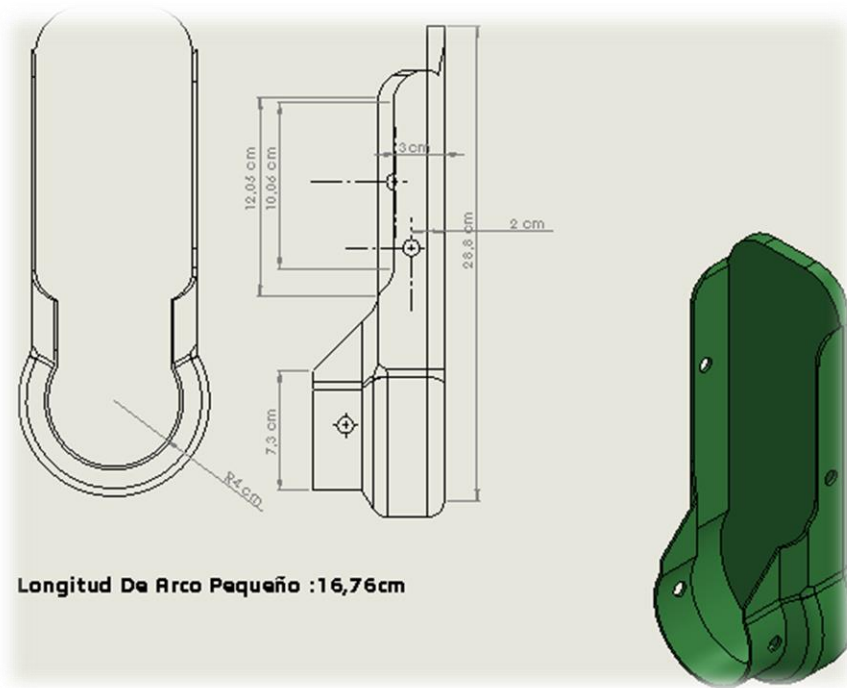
Ubicación de los actuadores en la pieza apoyo entre pierna
